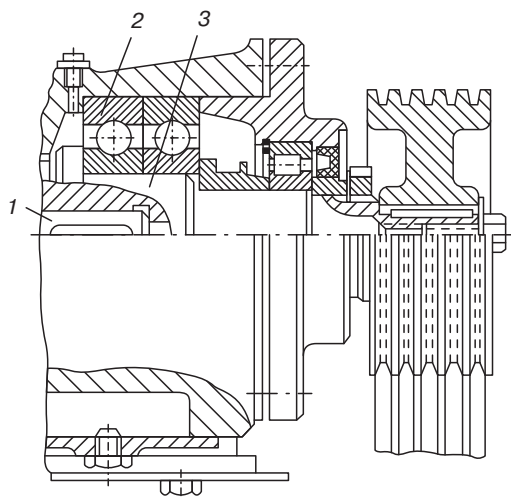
Схема узла подшипников быстроходного одношнекового экструдера
